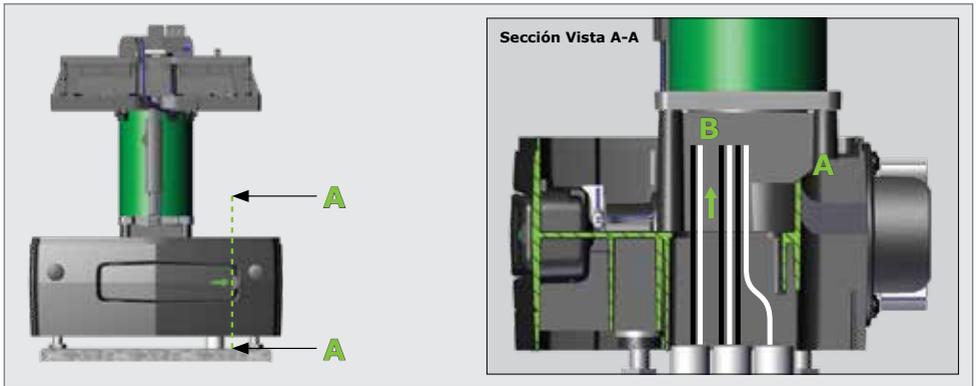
ENRUTAMIENTO DE CABLES PARA RETROAJUSTE CON CABLES MÁS CORTOS
